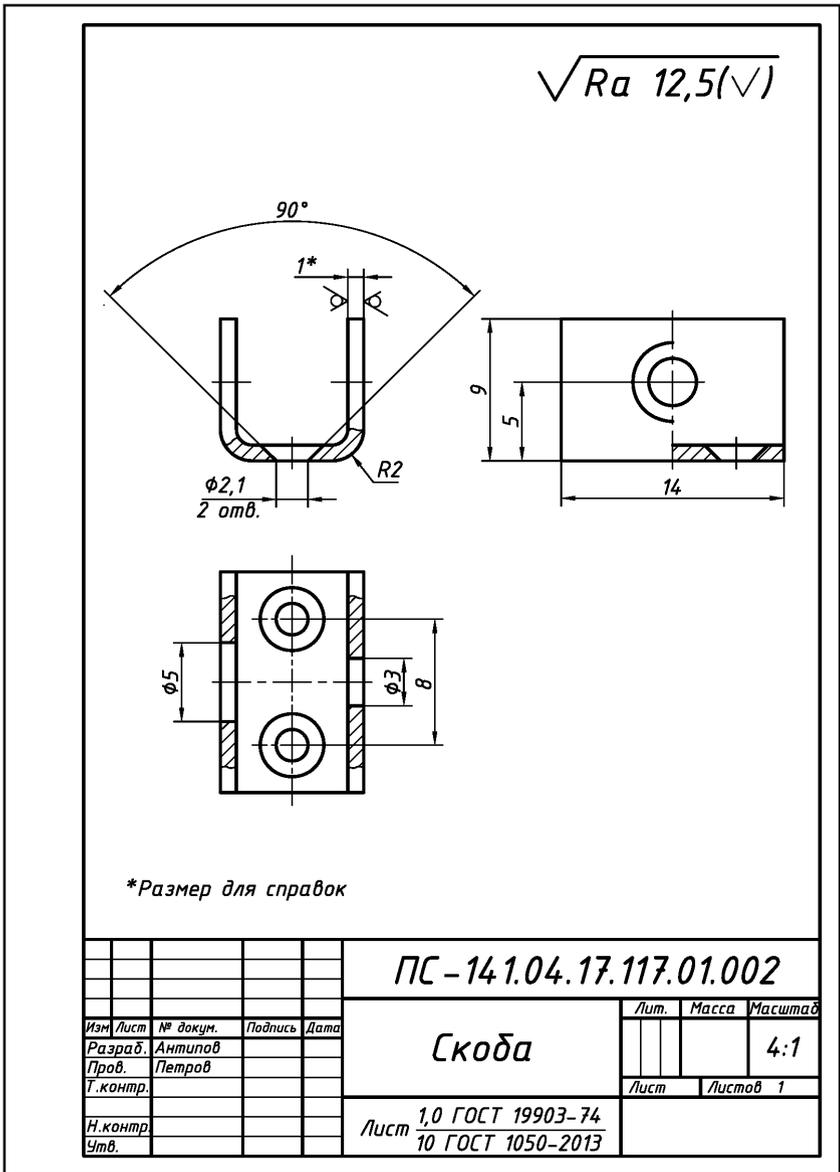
Оформление рабочего чертежа детали «Скоба»
